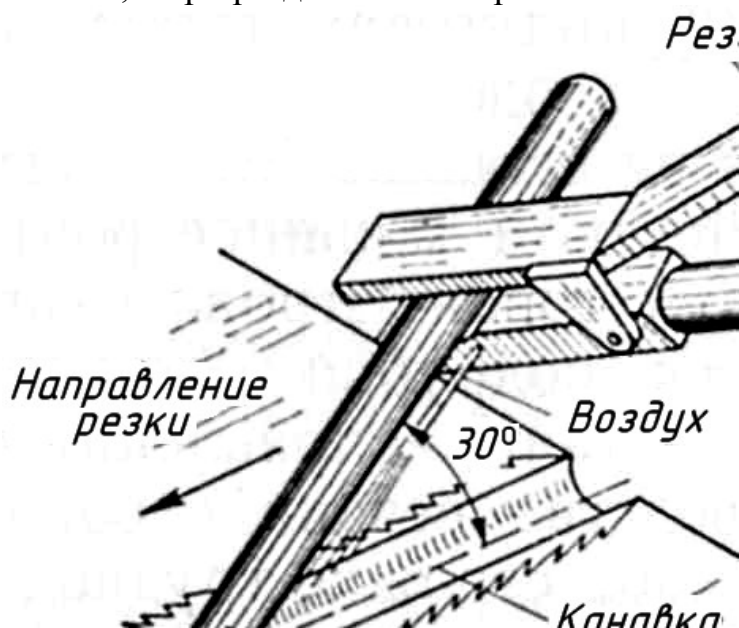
Схема поверхностной воздушно-дуговой резки
